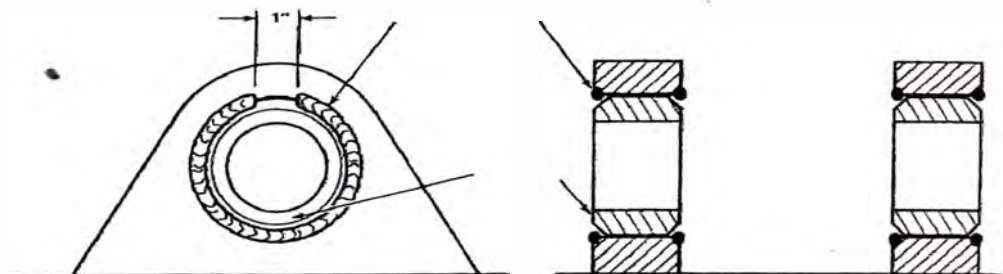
Soldadura de seguridad para el buje
